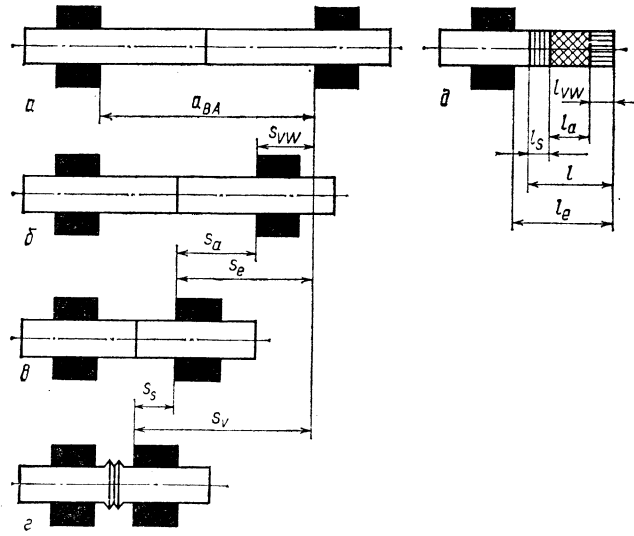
Технология и параметры стыковой сварки оплавлением:
